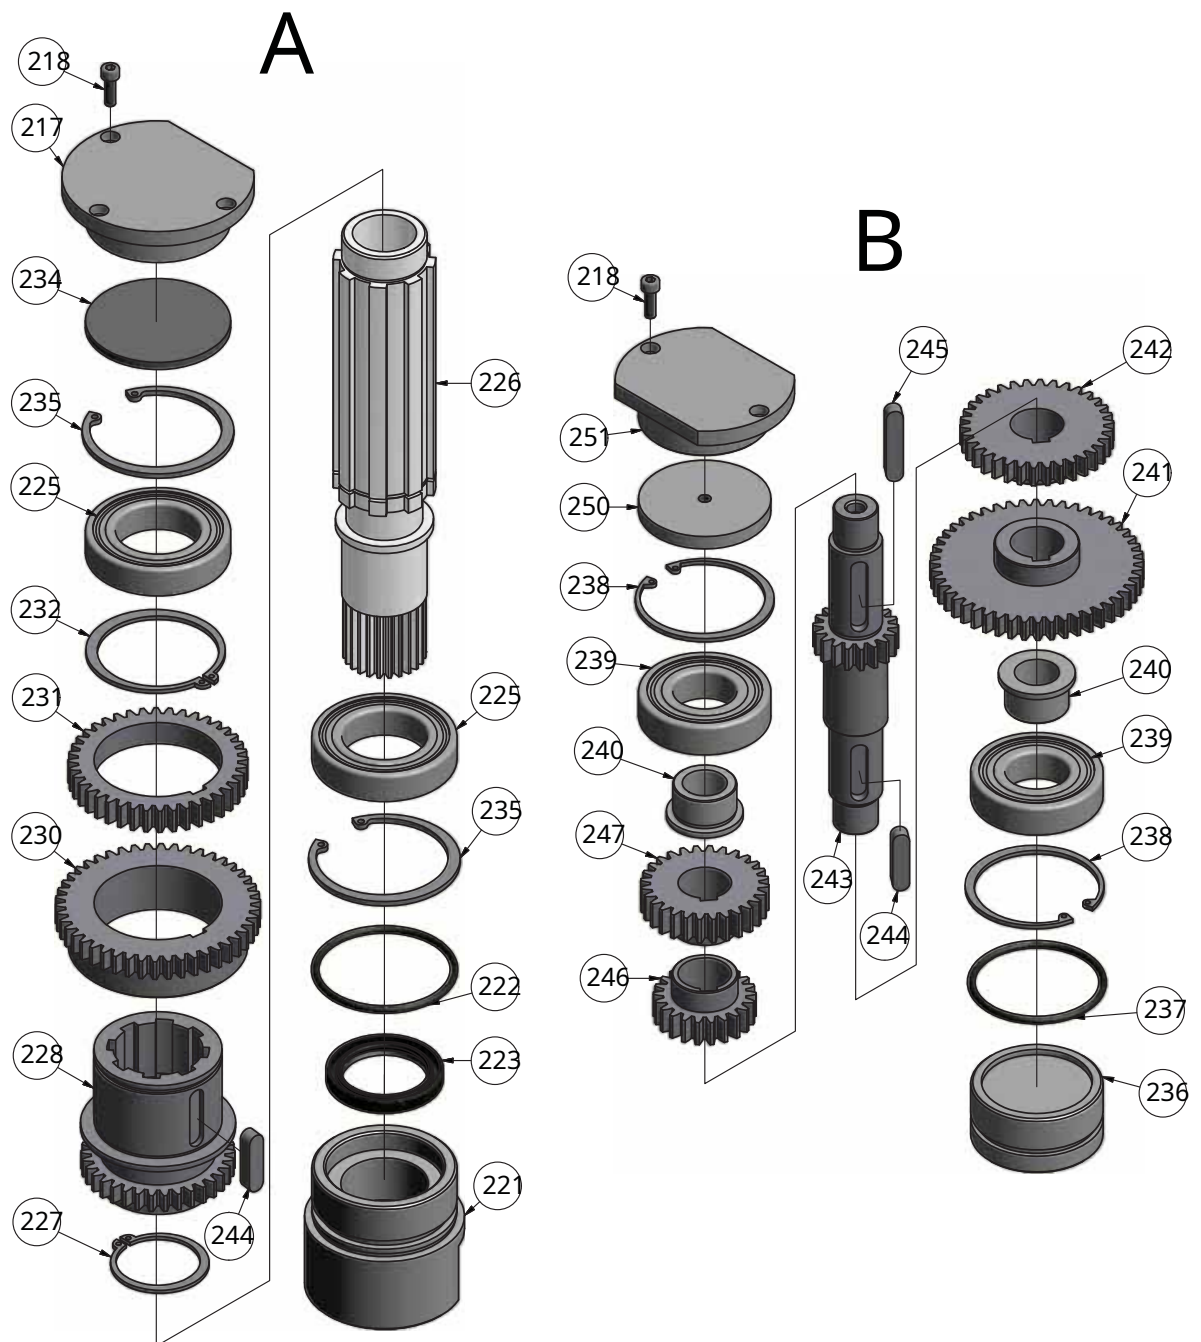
Getriebe Bohrspindel 1 de 4 - Husillo principal de caja de cambios 1 de 4
